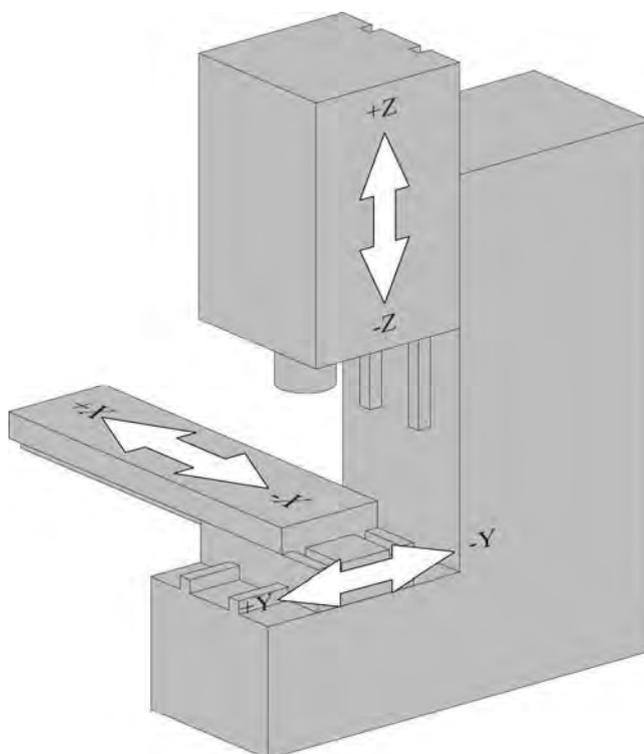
Схема фрезерного станка с ЧПУ для обработки зубьев сателлита
